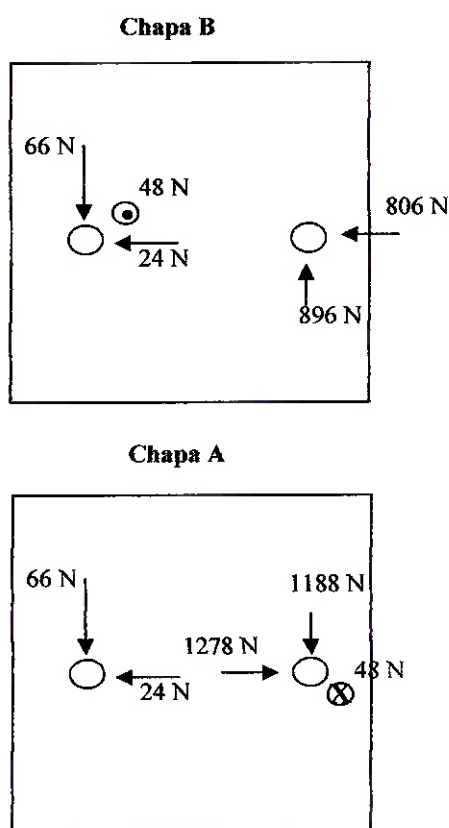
Forças Atuantes na Caixa de Engrenagem
